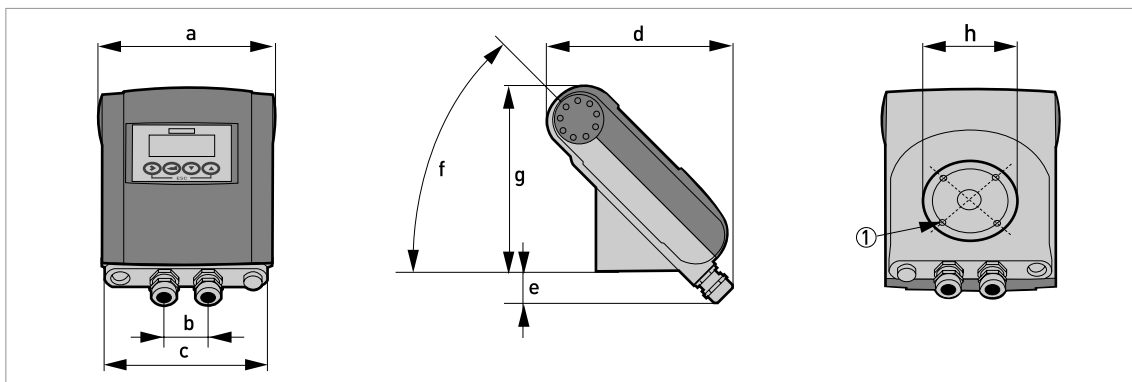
Abmessungen für Kompaktausführung (45°), Aluminiumgehäuse
